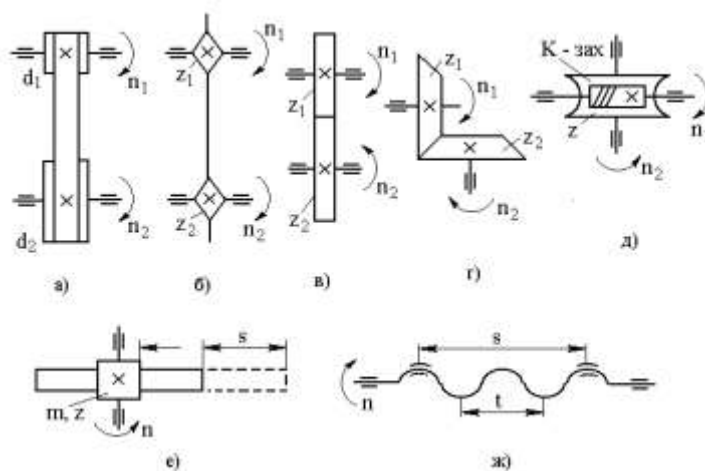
Основные типы передач металлорежущих станков: а – ременная; б – цепная; в, г – зубчатые; д – червячная; е – реечная; ж – винтовая
